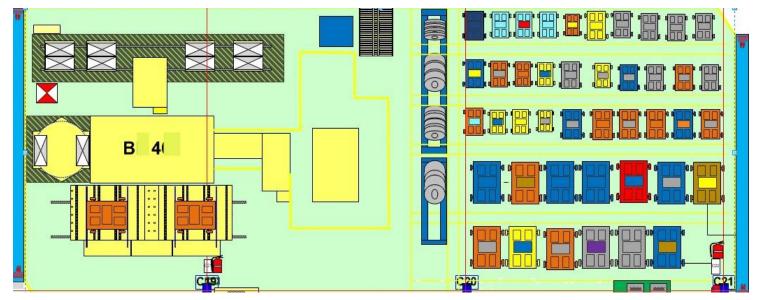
Layout Prensa Blankin 400 (actual)
